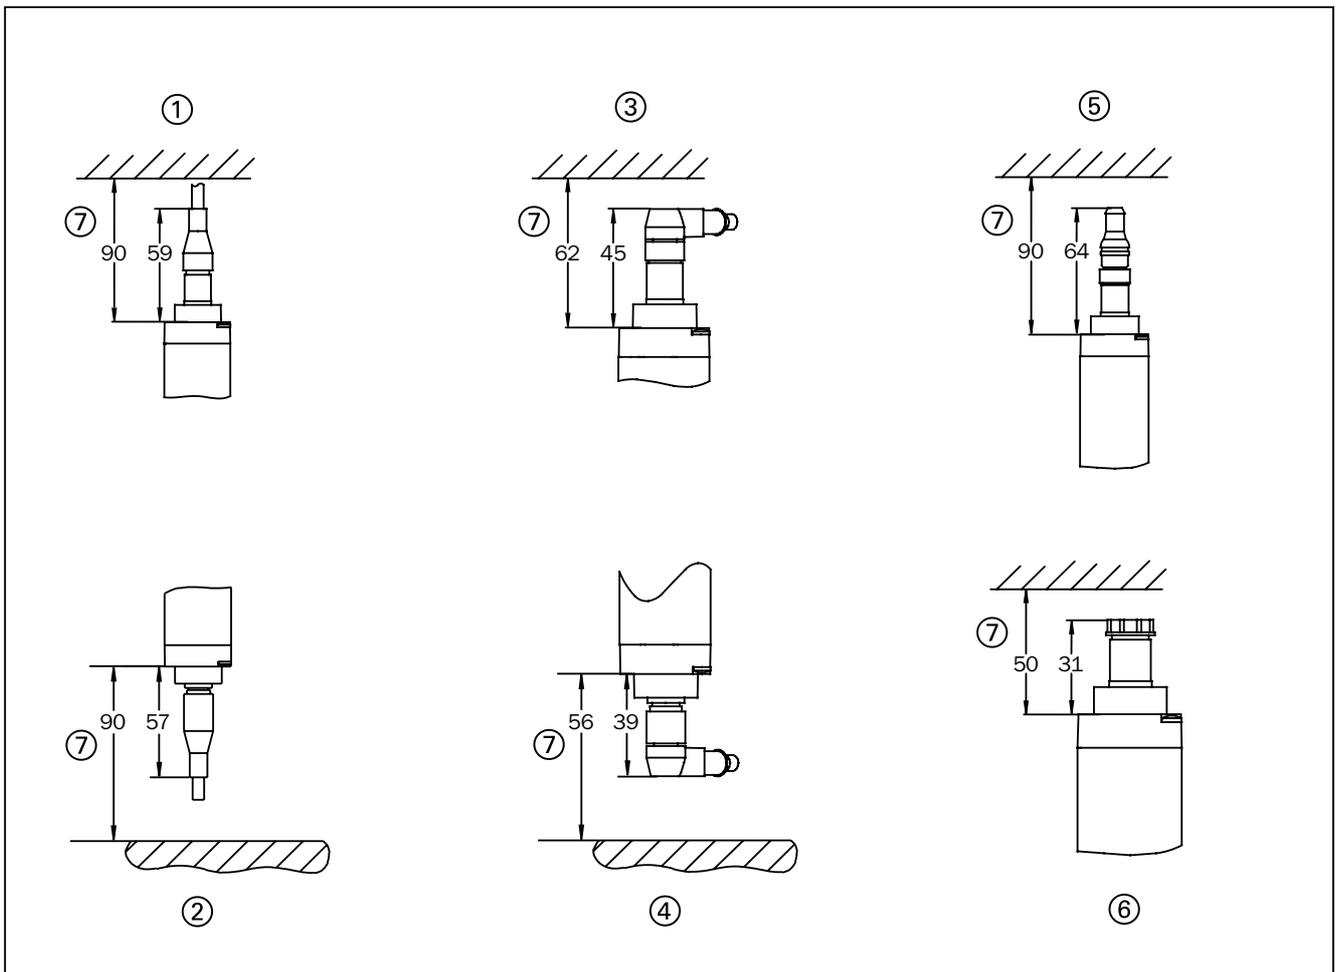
Plans et cotes d'encombrement des connexions pour les petits boîtiers
